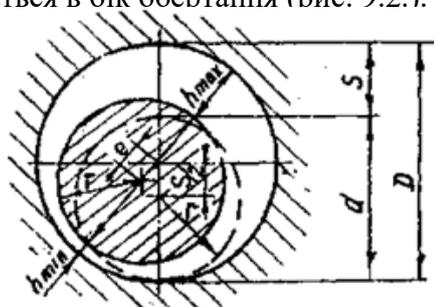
Схема розміщення вала в стані спокою і при усталеному режимі роботи підшипника
